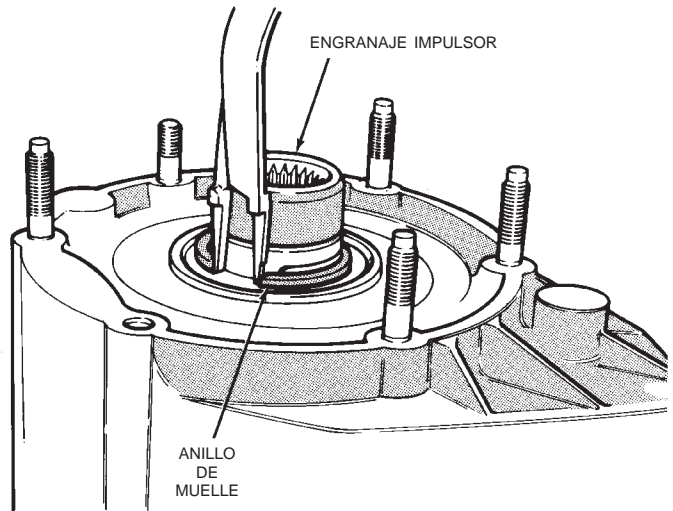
Instalación de anillo de muelle de engranaje de baja
